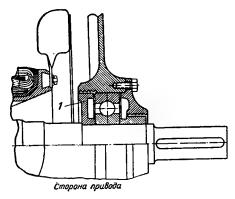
Подшипниковый узел с шарикоподшипником.
